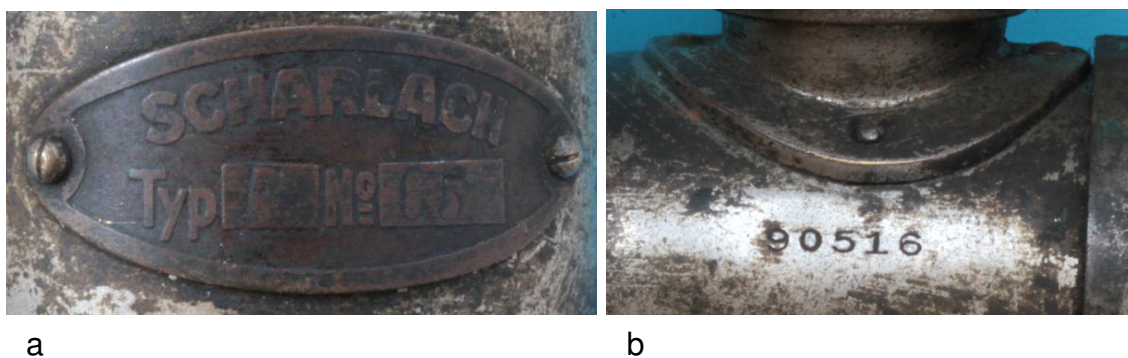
Beschriftungen: a) Typenschild, b) Fertigungsnummer 90516
